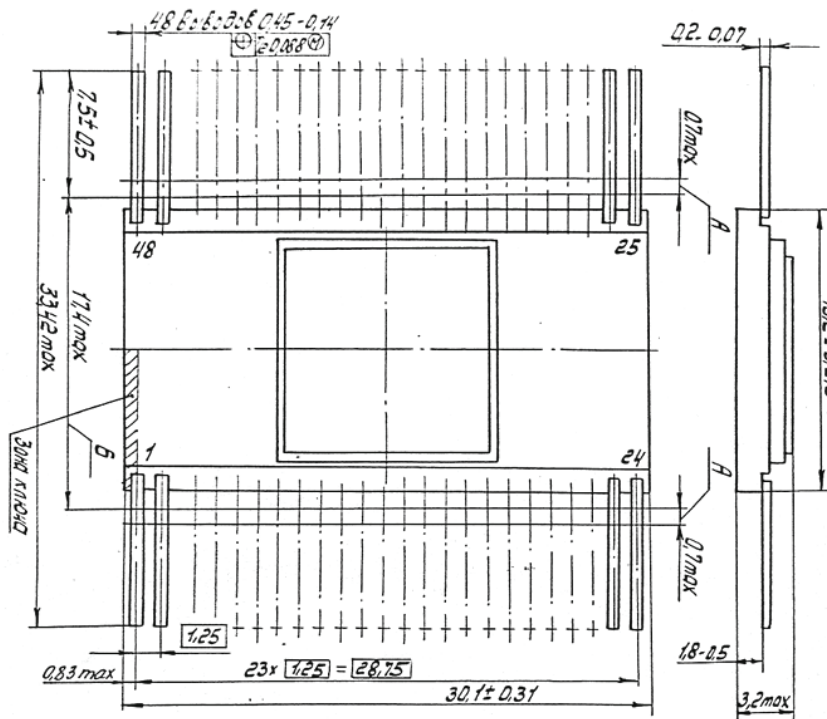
Габаритный чертеж корпуса 4134.48-2
